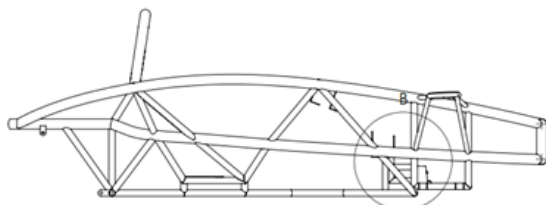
Detalle de acoplamiento de los soportes de la columna de dirección. Fuente: Autores.
